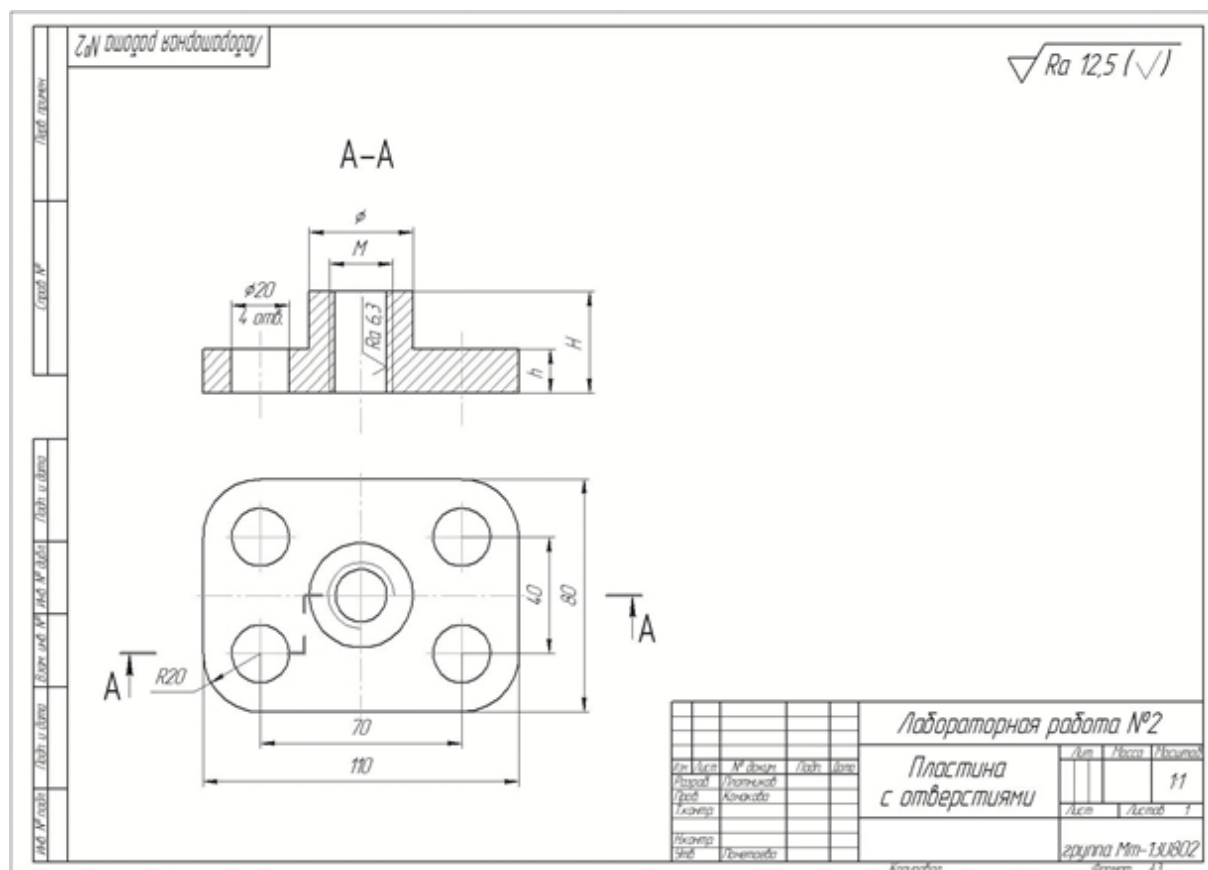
Чертеж детали со сложным ступенчатым разрезом
